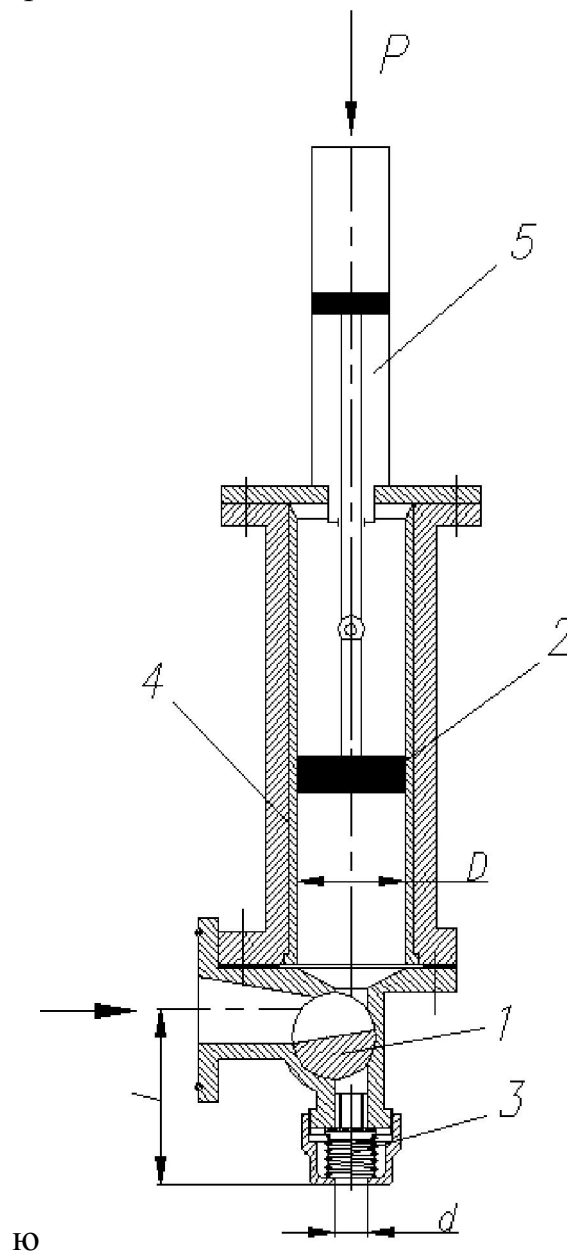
Розрахункова схема дозатора: 1 - поворотний кран; 2 - поршень; 3 - насадка; 4 - мірний циліндр; 5 – пневматичний циліндр.
